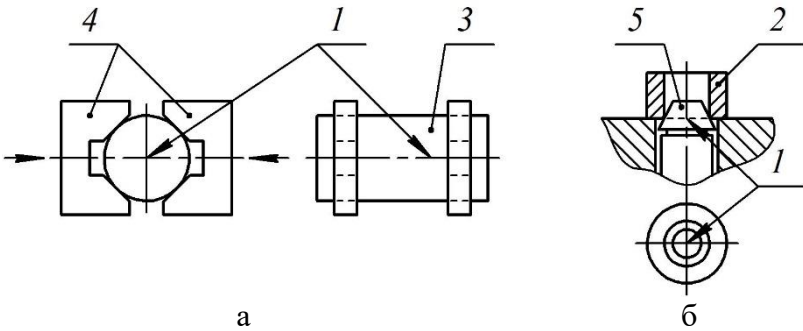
База (вісь і точка): 1 – базувальна поверхня, 2 – деталь, 3 – заготовка, 4 – губки самоцентрівних лещат, 5 – центрівний конус приладу
